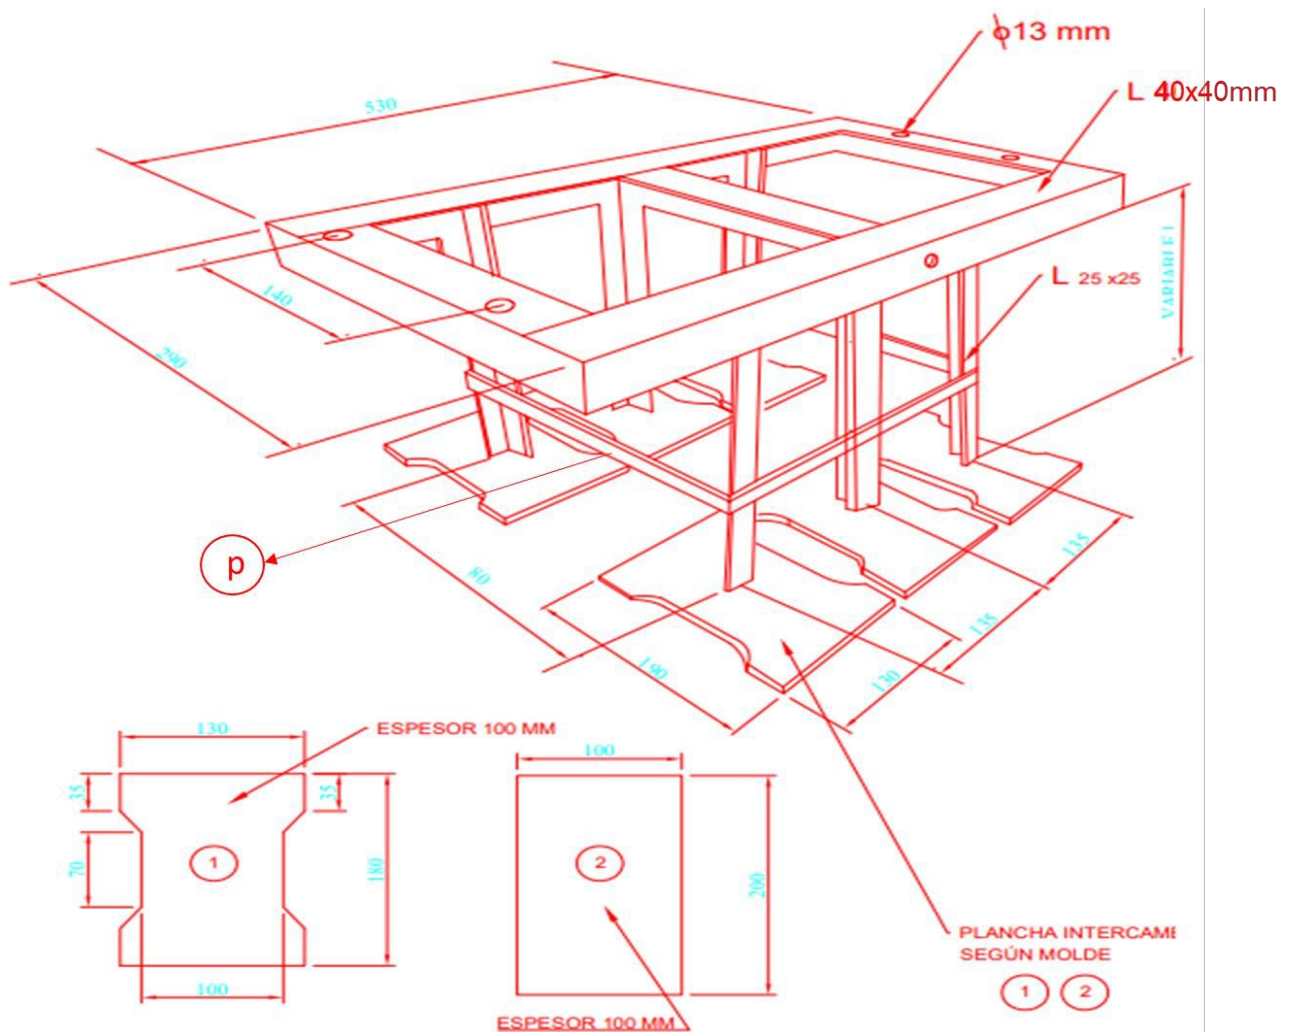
Parte superior de los moldes. Elaborado por el autor
